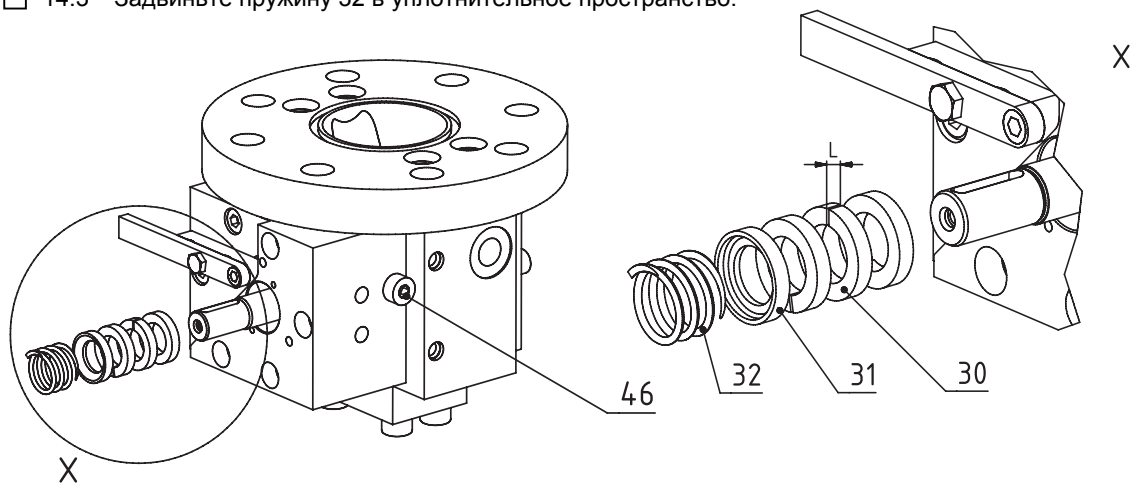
Задвиньте в корпус внутренние детали уплотнения вала; L = толщина сальникового кольца, O = разрез
